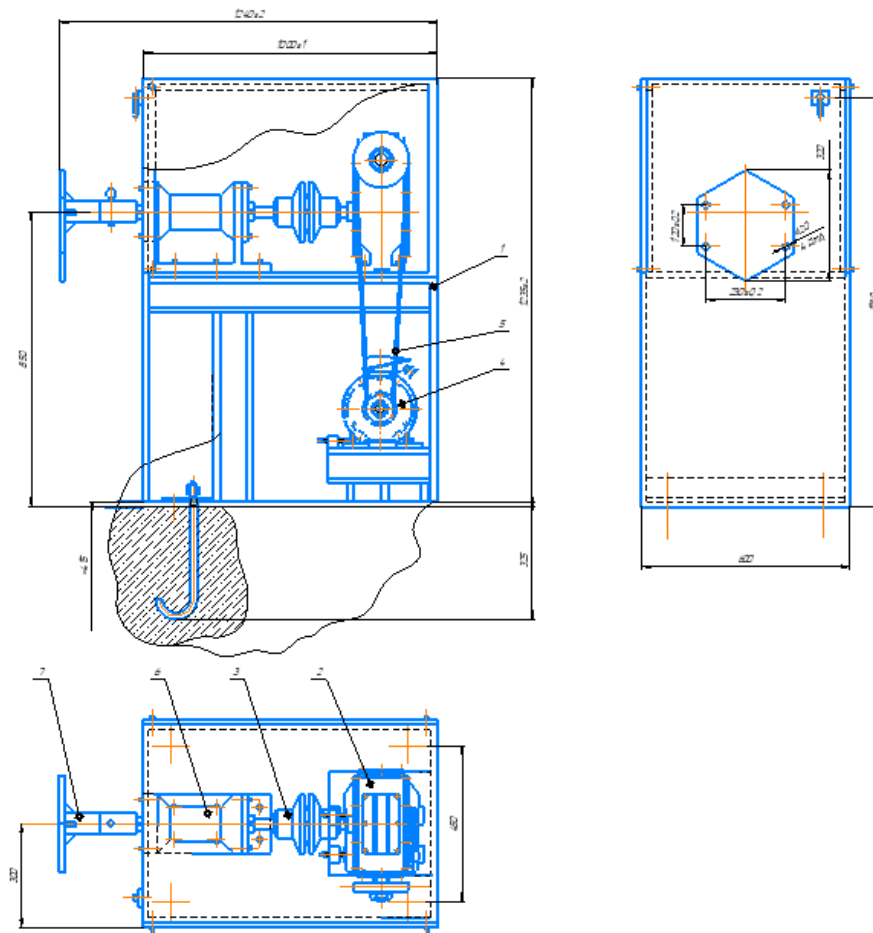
Стенд універсальний для розбирання-складання двигунів: 1 – рама; 2 – черв'ячний редуктор; 3 – муфта; 4 – електродвигун; 5 – клинопасова передача; 6 – опора; 7 – фланець
